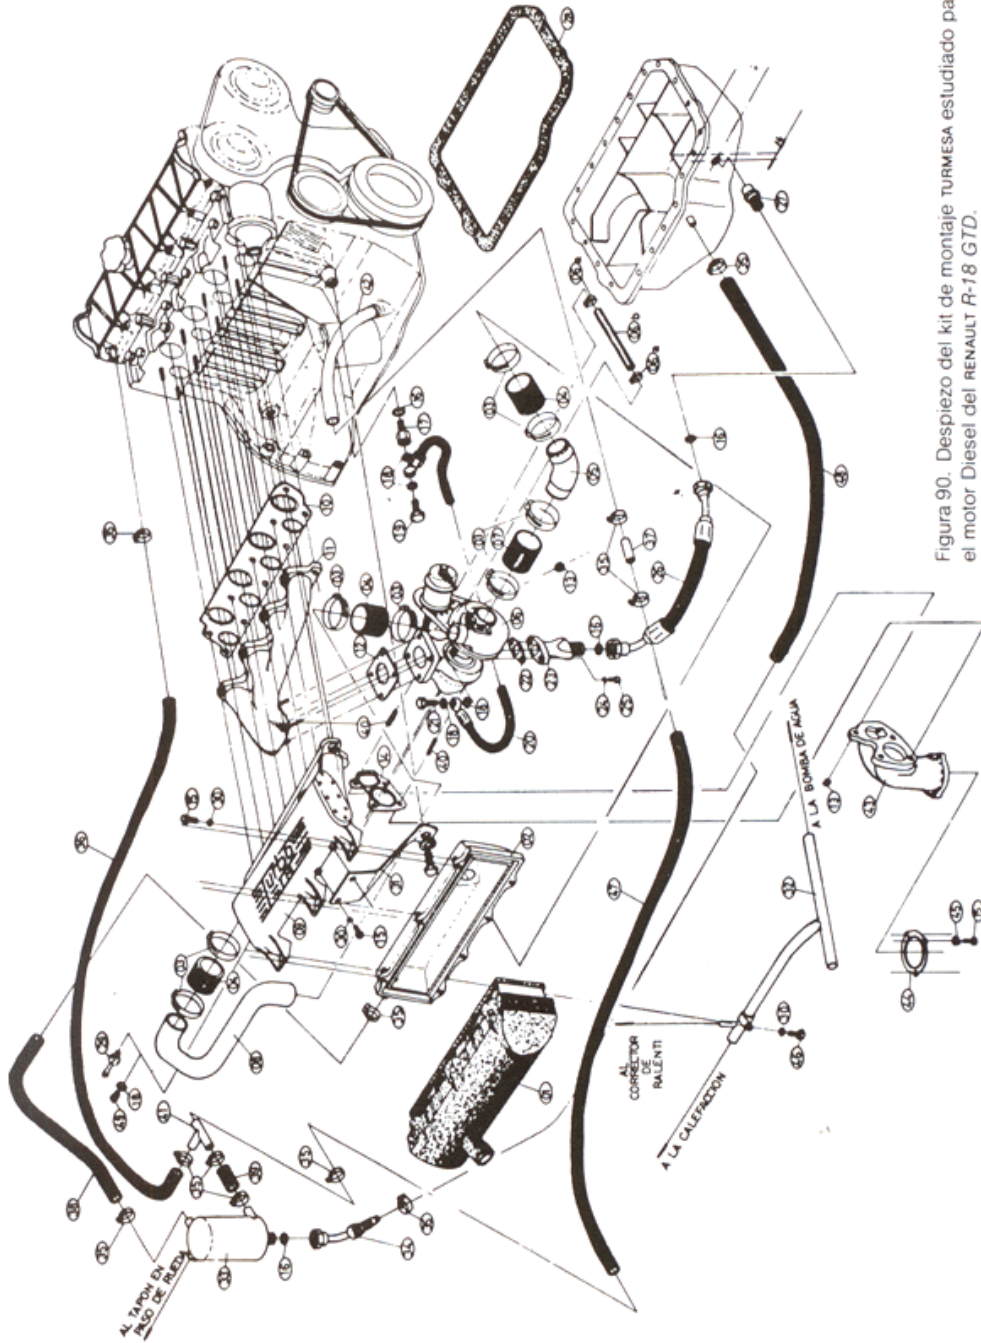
Despiece del kit de montaje TURMESA estudiado para el motor Diesel del RENAULT R-18 GTD.
